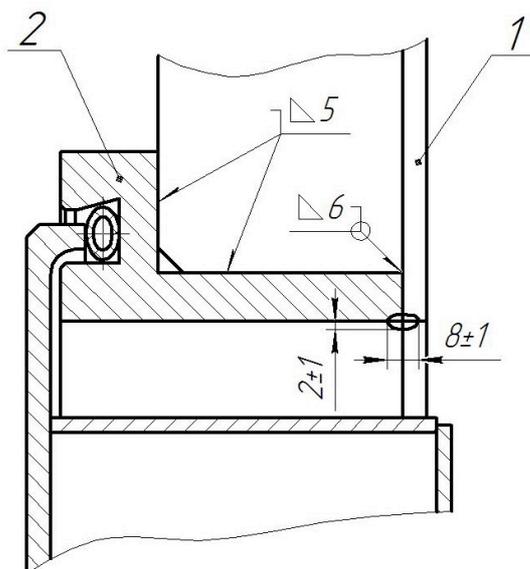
Сварка фланцев батареи циклонов и бункера
